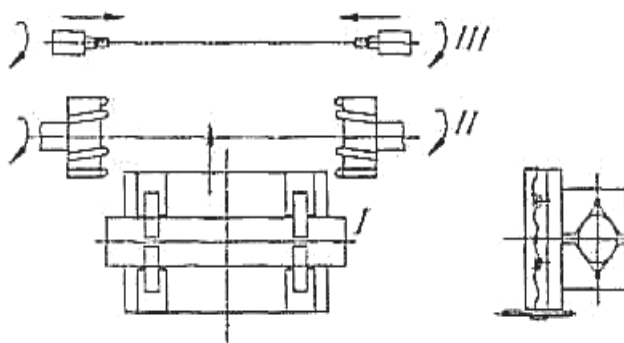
Схема обработки вала на фрезерно-центровальном станке
